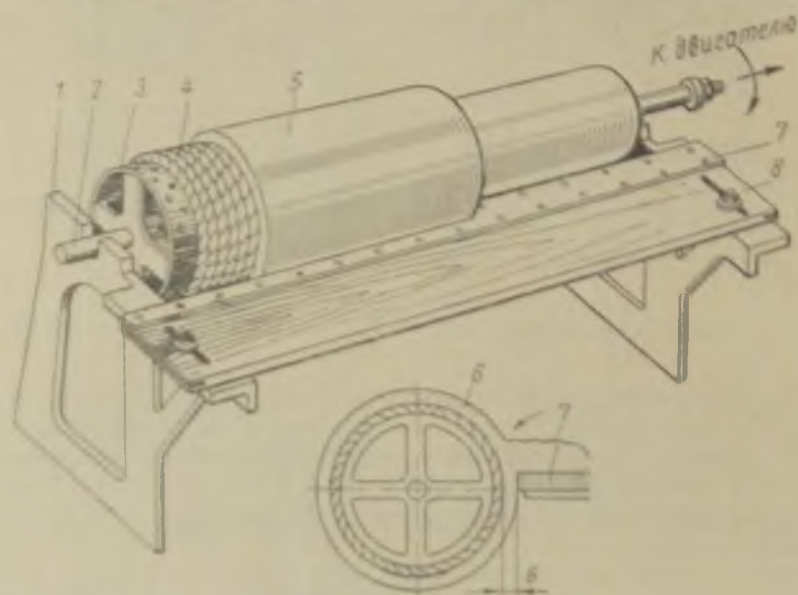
Изготовление цилиндрического стержня при помощи шаблона
